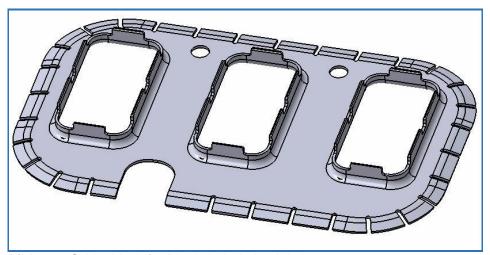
Schirmblech für Ringkabelschuh mit Leitung
